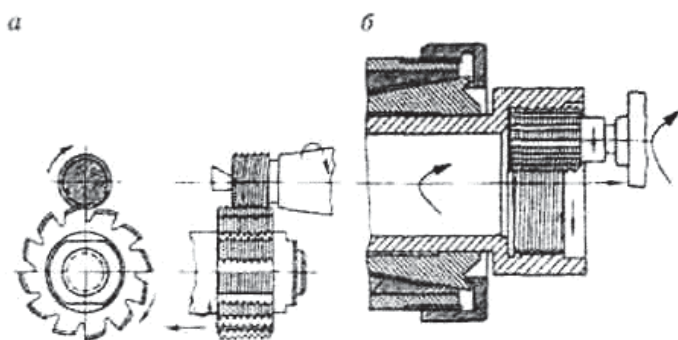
Схемы фрезерования резьбы групповыми фрезами
